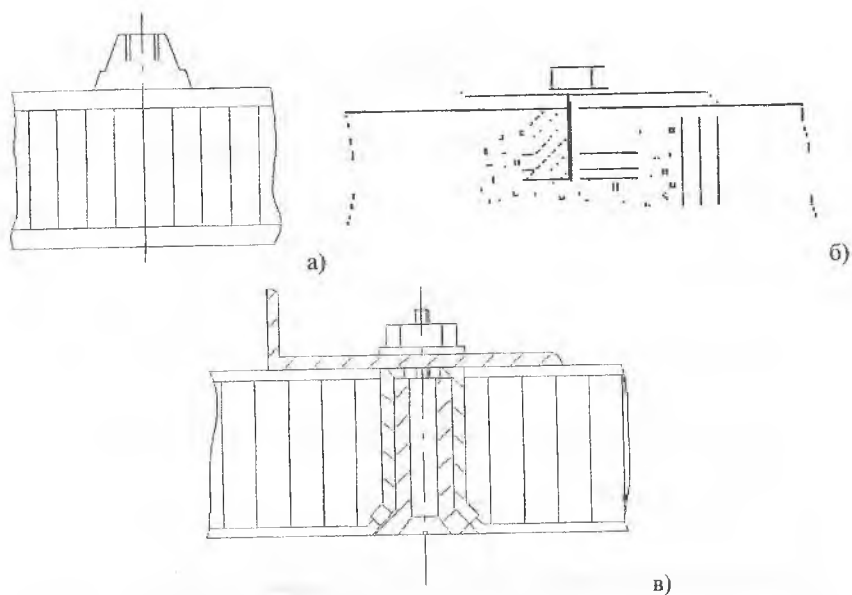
Способы закрепления вкладышей в отверстиях трехслойной конструкции: а) сваркой; б) клеевым соединением; в) телескопическим соединением
